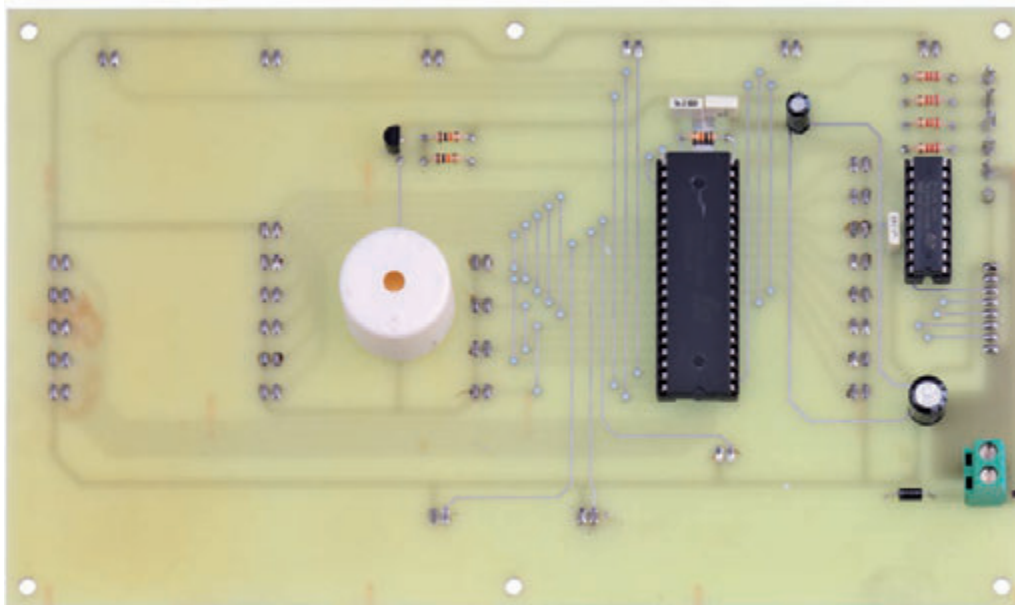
Photo d'un des prototypes de la platine EN1760 vue du côté composants.
